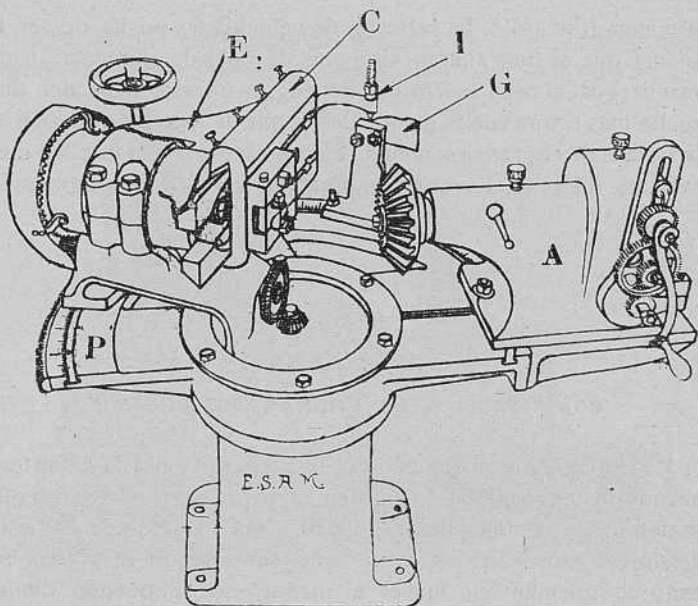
Cepilladora de engranajes cónicos E. S. A. M.
